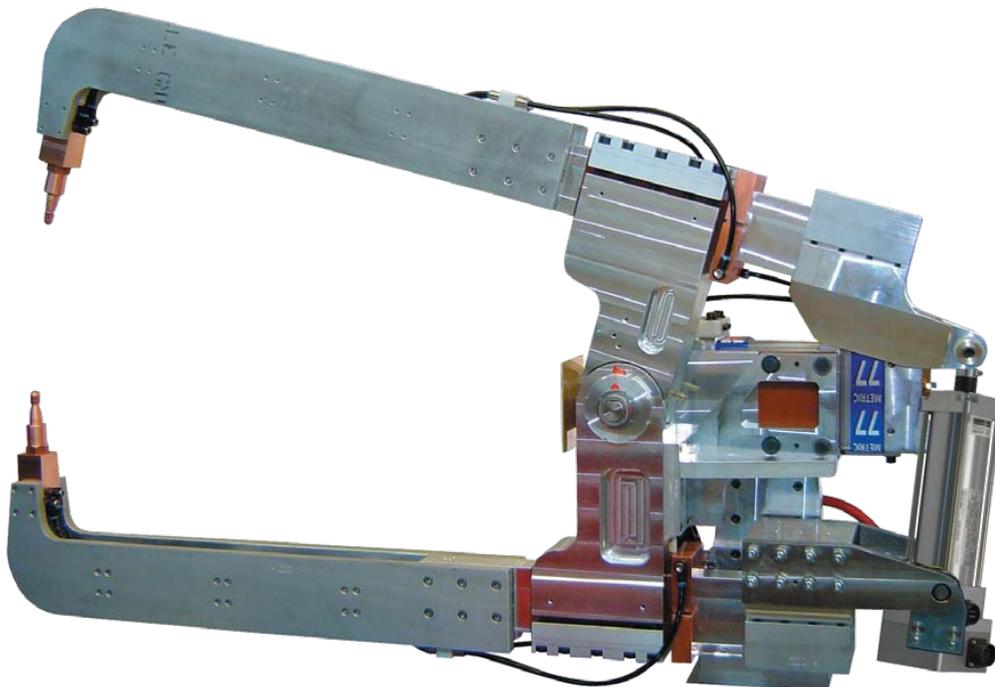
Ejemplo de actuador ServoWeld instalado en la unidad de pistola de soldar estilo "X".
